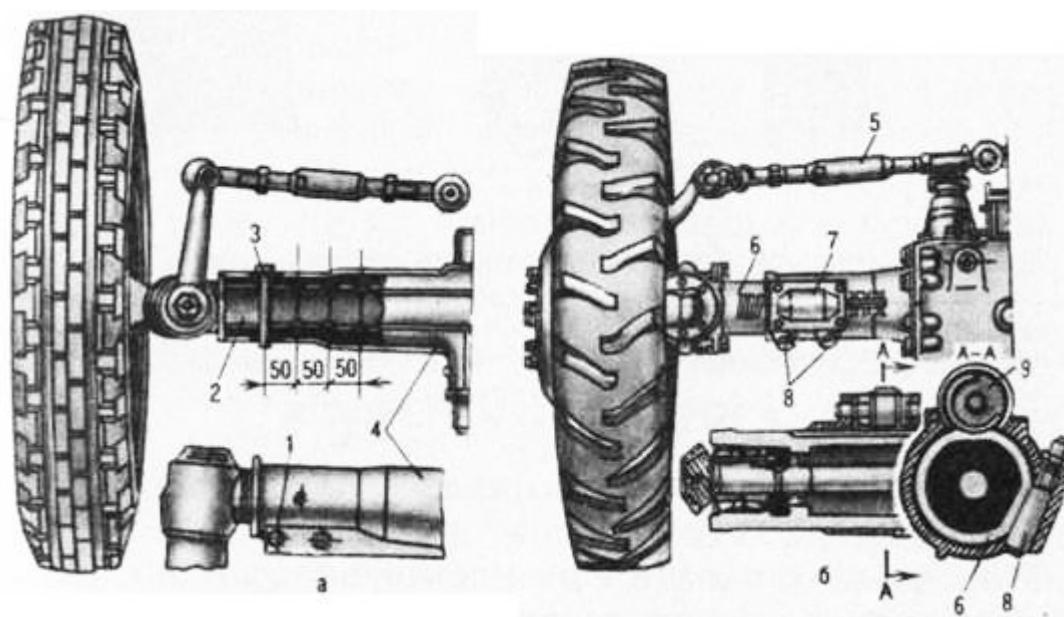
Устройства для расстановки ширины колеи передних колес трактора: а — ступенчатое; б — плавное; 1 — болт; 2 — выдвижной кулак; 3 — палец; 4 — балка; 5 — рулевая тяга; 6 — корпус; 7 — крышка; 8 — клинья; 9 — червяк.
